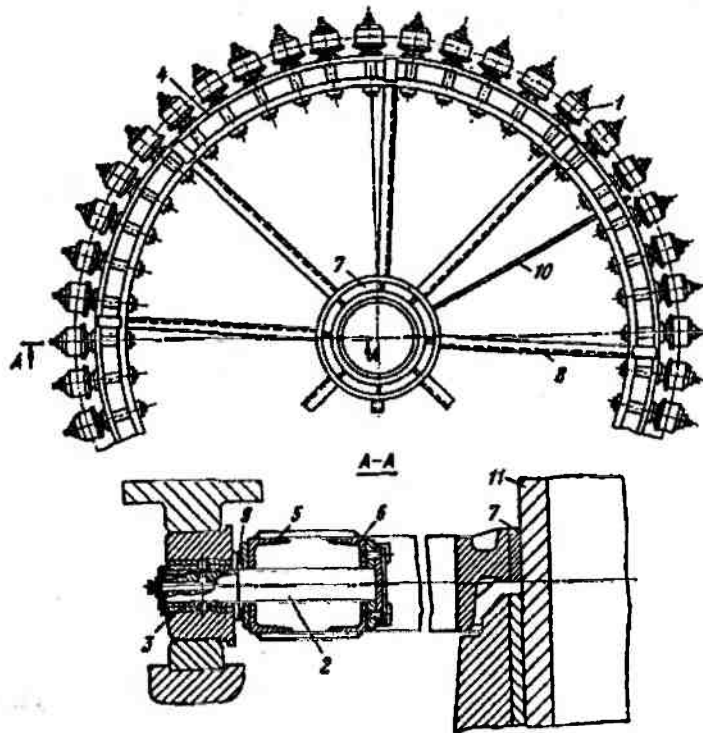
Опорно-поворотное устройство со свободными роликами экскаватора ЭКГ-10
